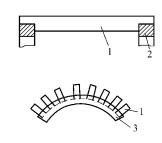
端环与铜条的焊接结构 1—导条 2—端环断面 3—端环
